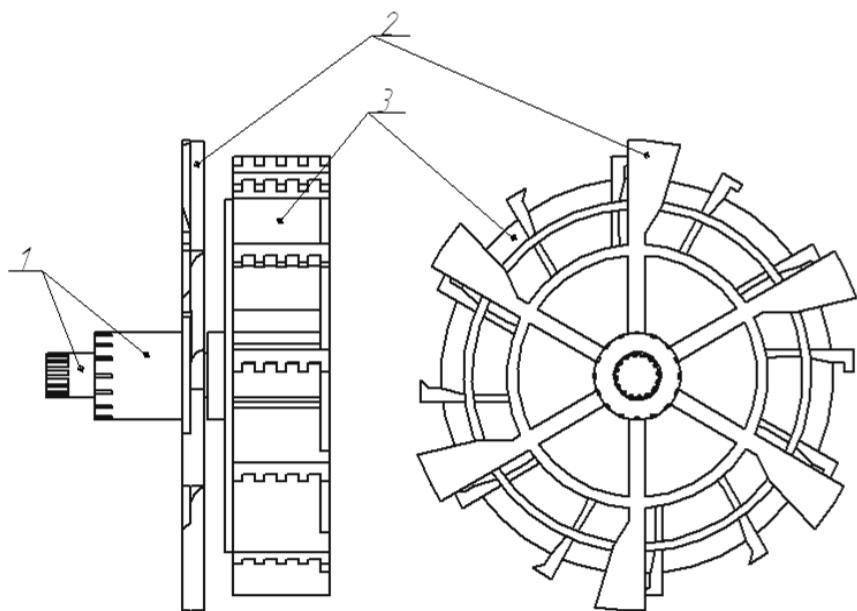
Схема рабочего органа пожарного грунтотема: 1 – приводные валы; 2 – роторная фреза разрыхлитель почвы; 3 – роторная фреза метатель почвы.
